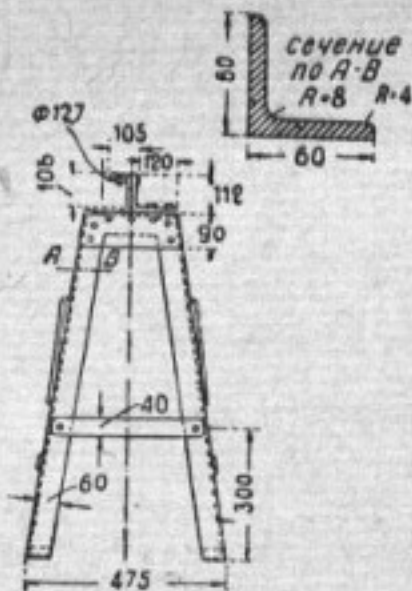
Приспособление для запрессовки шкворней и выпрессовки кронштейнов передней оси
